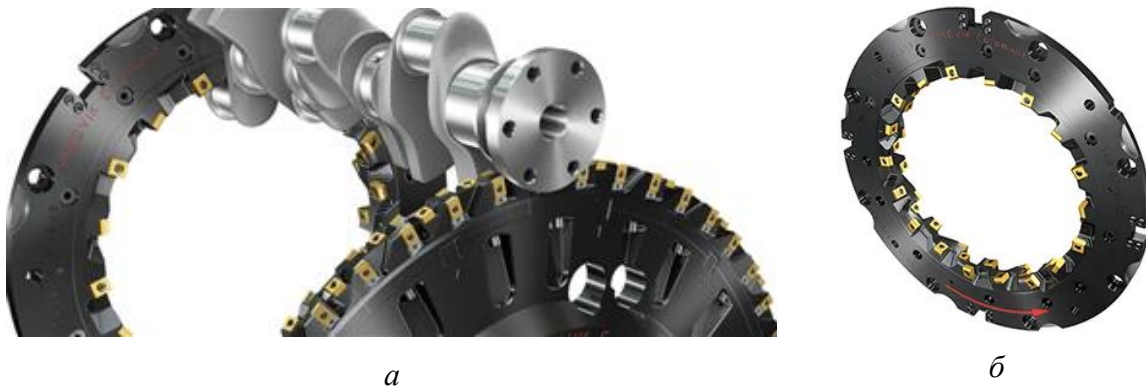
Фрезерування колінчастих валів (а) та фреза (б) [12]
